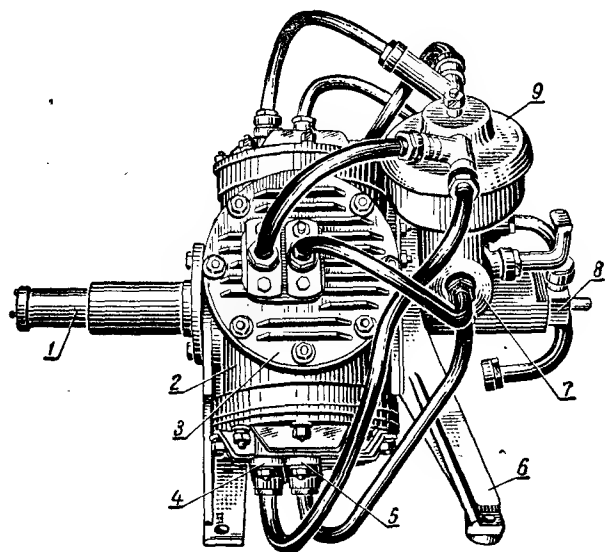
Мембранный компрессор агрегата «Вихрь» (ВНП-4М):
